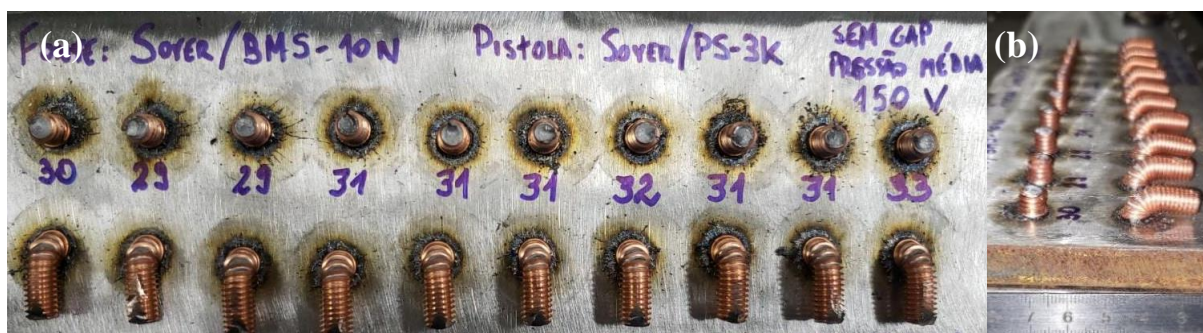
Pinos M8 soldados na chapa de 12,7 mm de espessura após os testes de dobramento e de torque.
